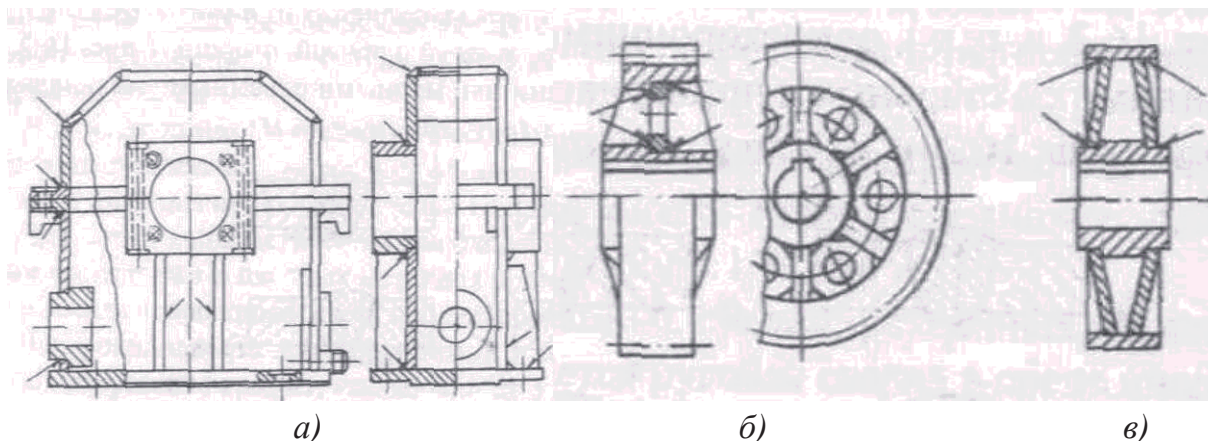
Сварные заготовки: *а* – корпуса червячного редуктора; *б* – зубчатого колеса; *в* – шкива
